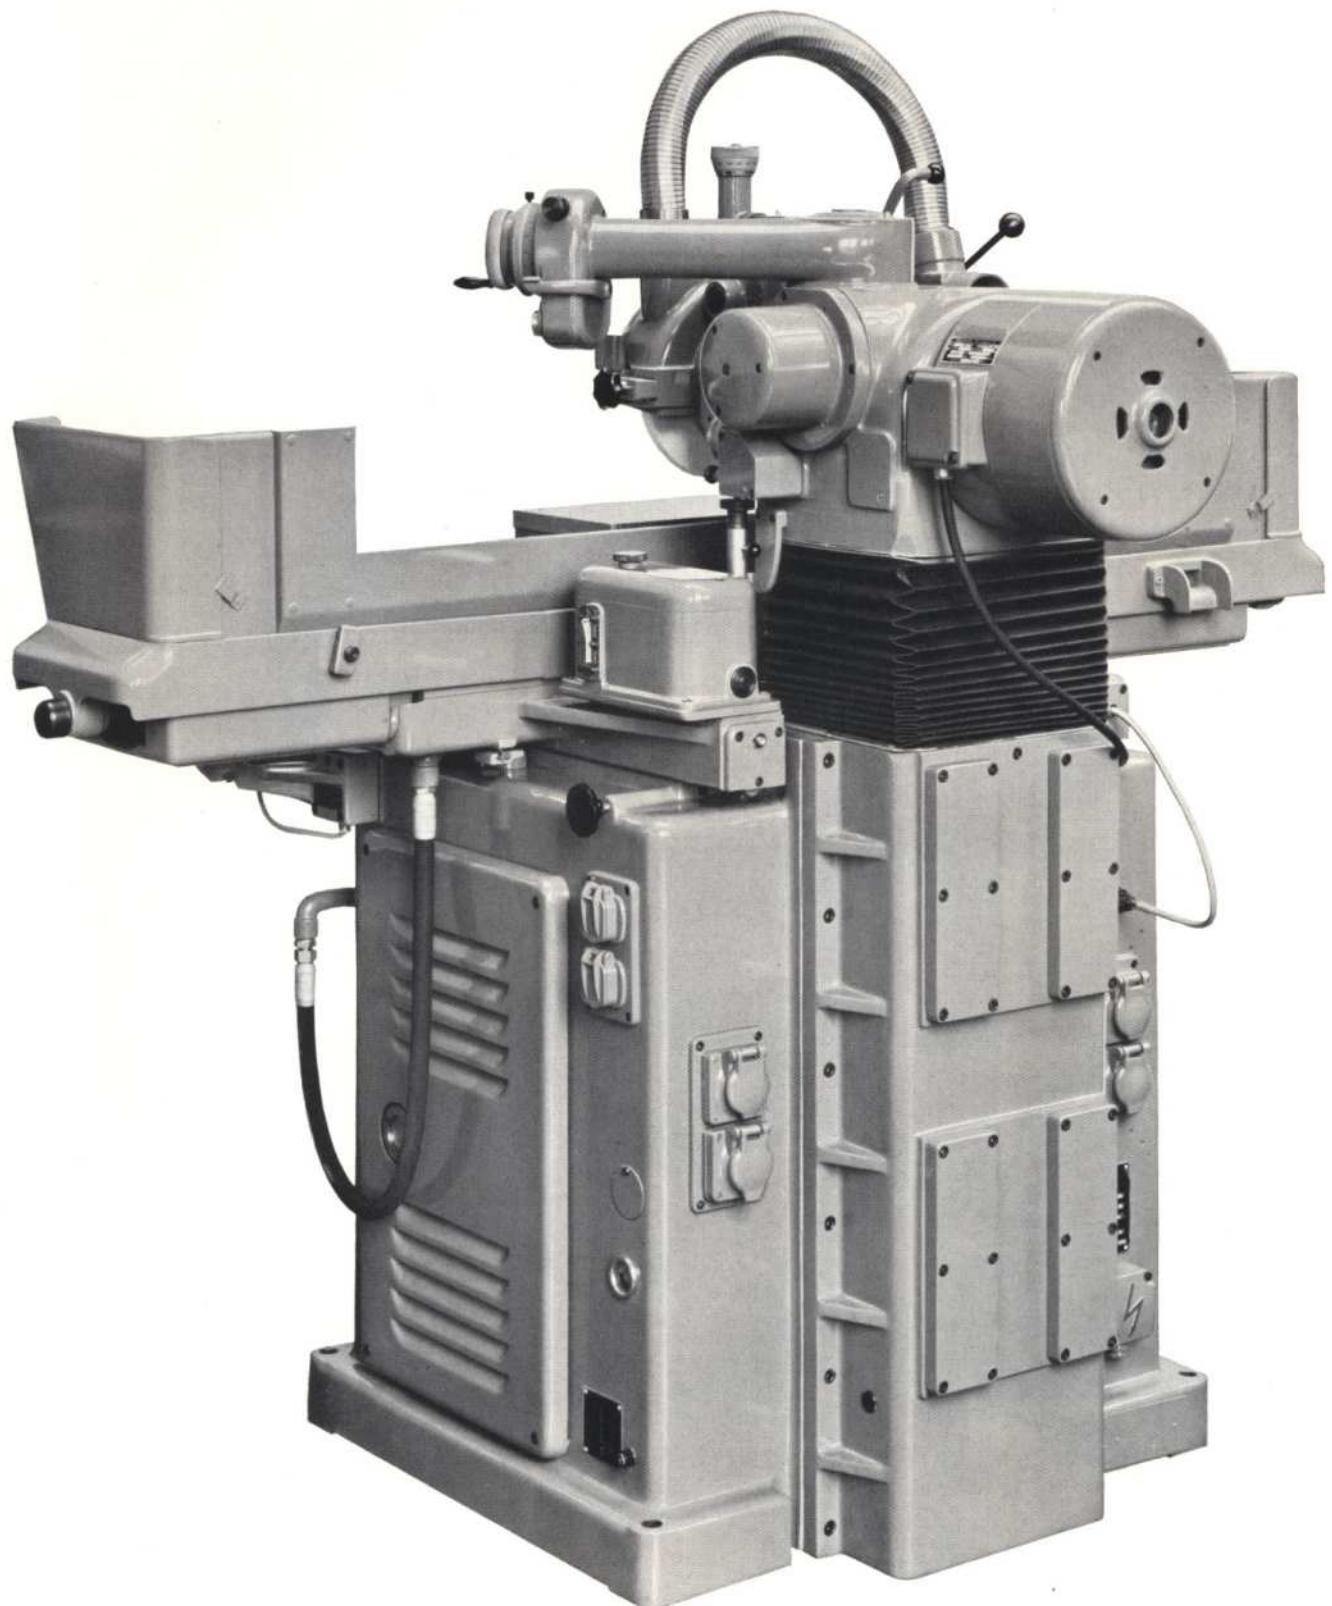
zeigt die Rückansicht der Maschine F 50 mit Regelantrieb
